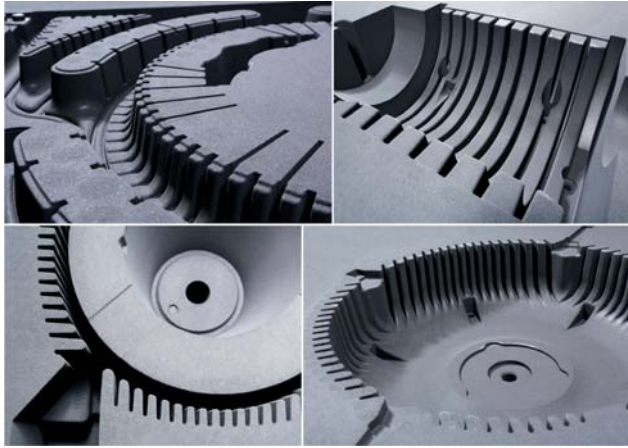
Пример уровня сложности и качества форм по Сейятцу-процессу для отливок с тонкими длинными ребрами, например «Корпуса электродвигателя»
